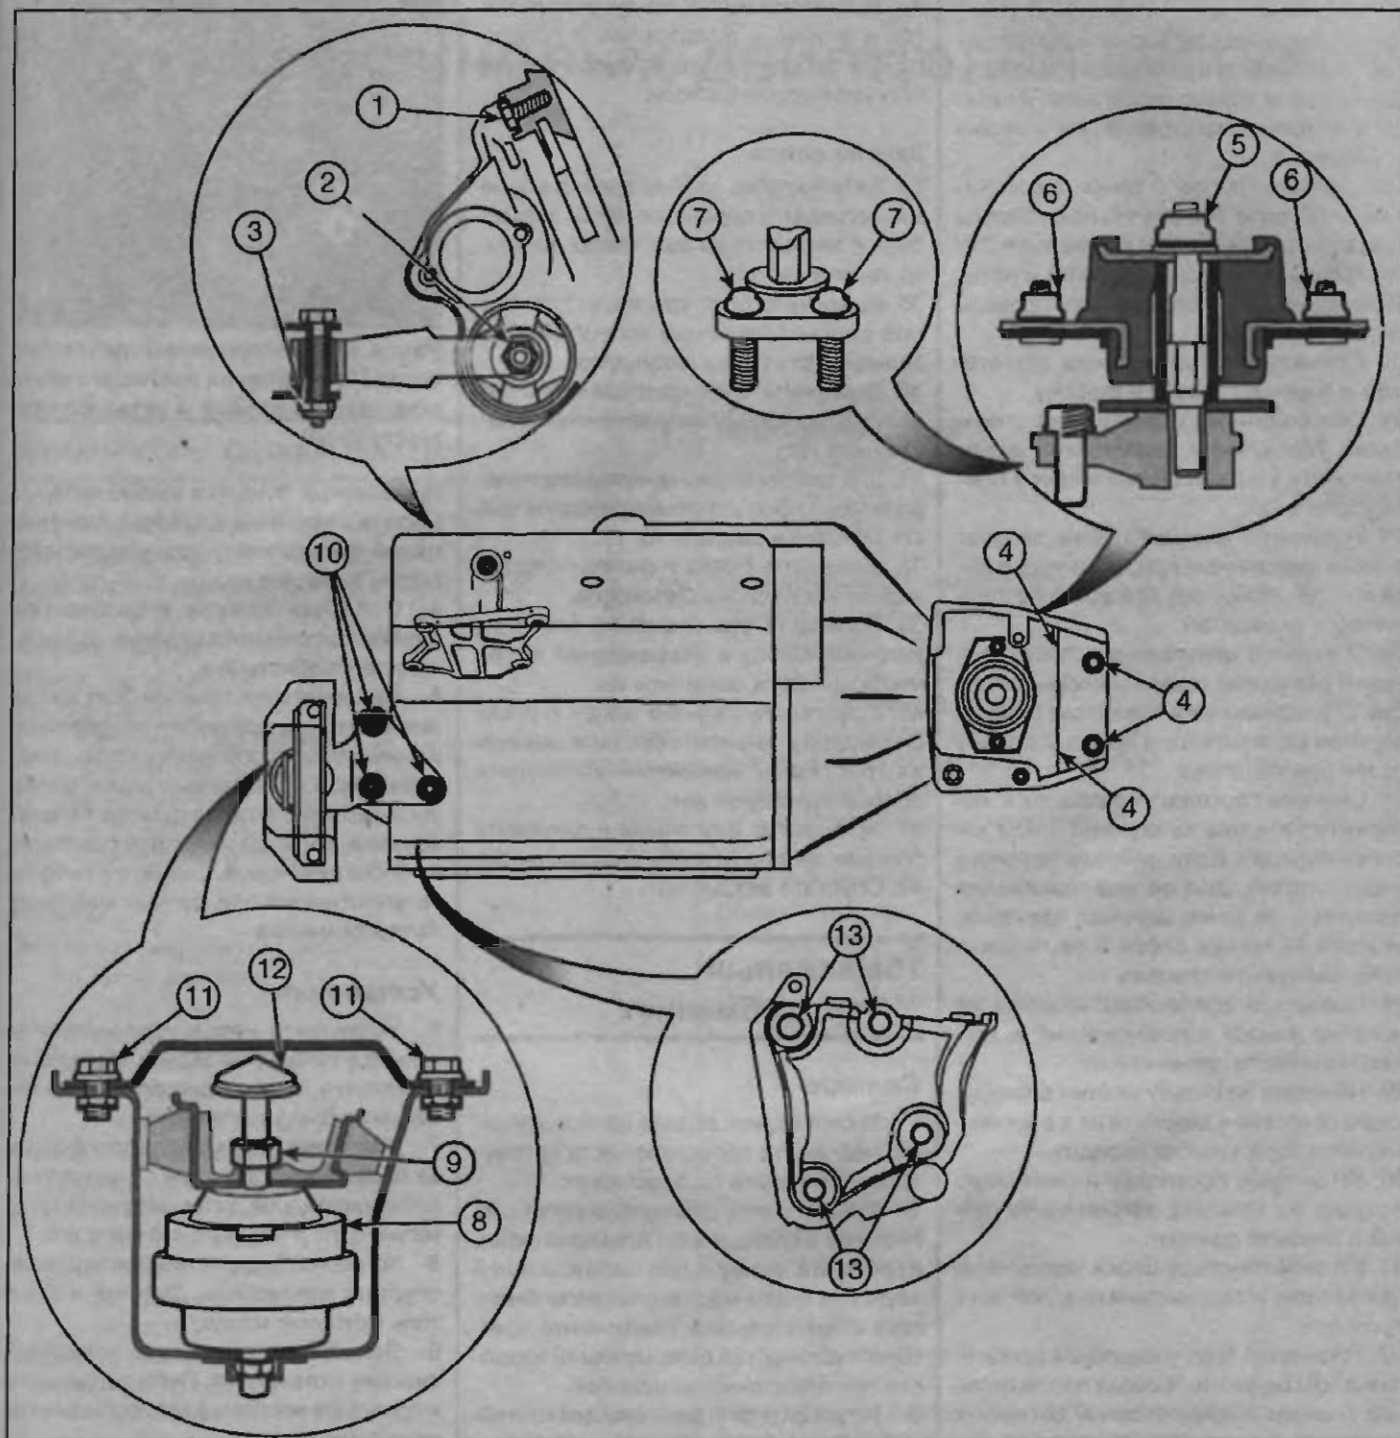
Опоры двигателя/коробки передач: 1 – болты крепления кронштейна задней опоры к блоку цилиндров; 2 – болт крепления задней опоры, соединяющий тягу с кронштейном блока цилиндров; 3 – болт крепления задней опоры, соединяющий тягу с нижней рамой; 4 – болт крепления кронштейна левой опоры к кузову; 5 – центральная гайка крепления резиновой подушки левой опоры; 6 – гайки крепления левой резиновой подушки к кронштейну; 7 – болты крепления кронштейна левой опоры к коробке передач; 8 – правая резиновая подушка; 9 – гайка крепления кронштейна к резиновой подушке правой опоры; 10 – болты крепления верхнего кронштейна к нижнему кронштейну правой опоры; 11 – болты крепления кронштейна жесткости правой опоры; 12 – центральная гайка крепления резиновой подушки правой опоры; 13 – болты крепления нижнего кронштейна правой опоры
